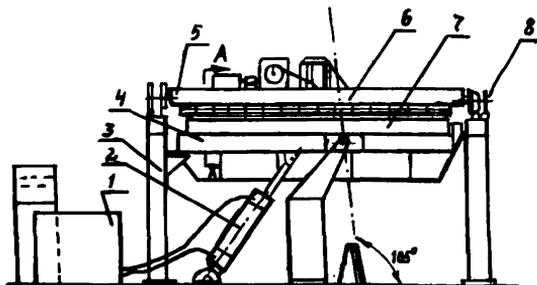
Установка для шпаклевки железобетонных и бетонных поверхностей:
